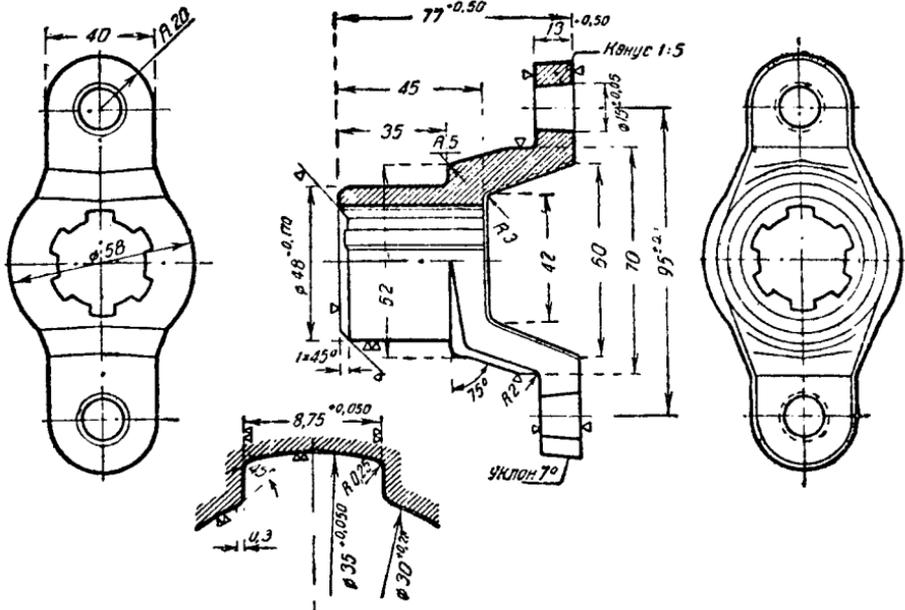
Дет. 18-49. Передняя вилка гибкой муфты сцепления
